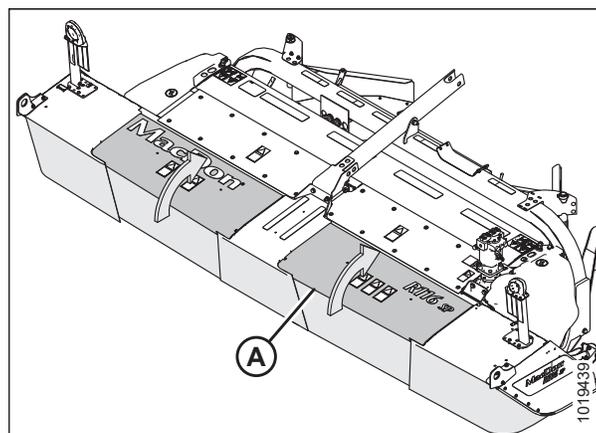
Дверки и шторки ножевого бруса (показано для R116, R113 аналогично)
